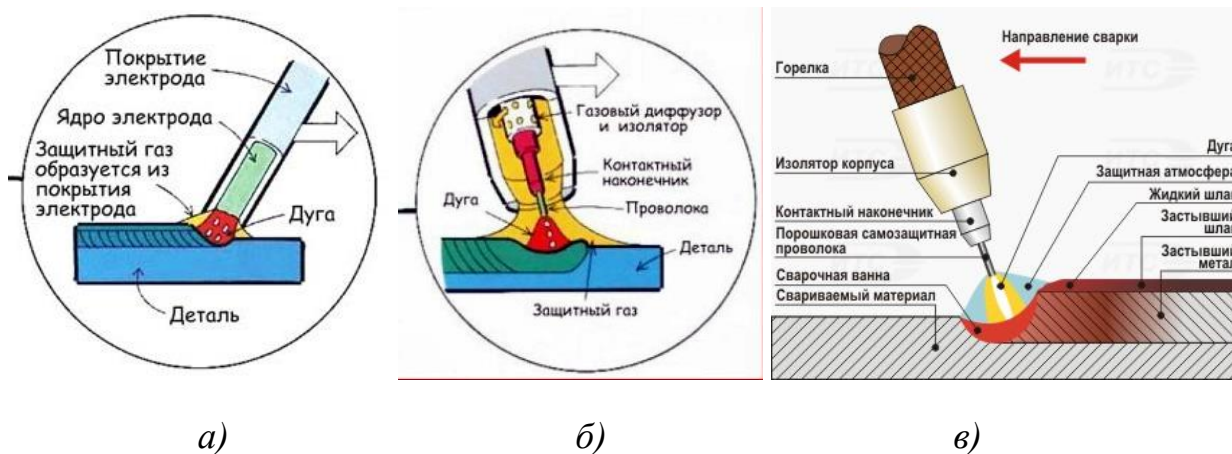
Рассматриваемые способы ремонтной сварки: ручная дуговая (а), в защитном газе проволокой сплошного сечения (б), самозащитной порошковой проволокой (в)
